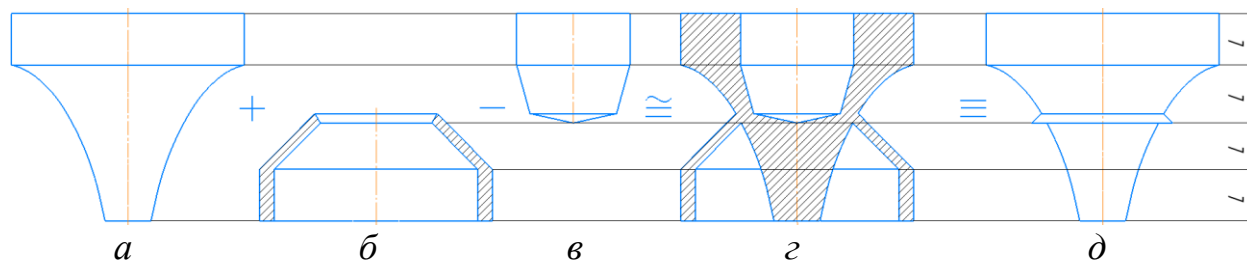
Способ обеспечения бойка двумя посадочными поверхностями: а – исходный боёк, б – оболочка, в – отверстие, г – боёк с двумя цилиндрическими посадочными поверхностями, д – приведенная цельнотельная форма бойка (составлено автором)
